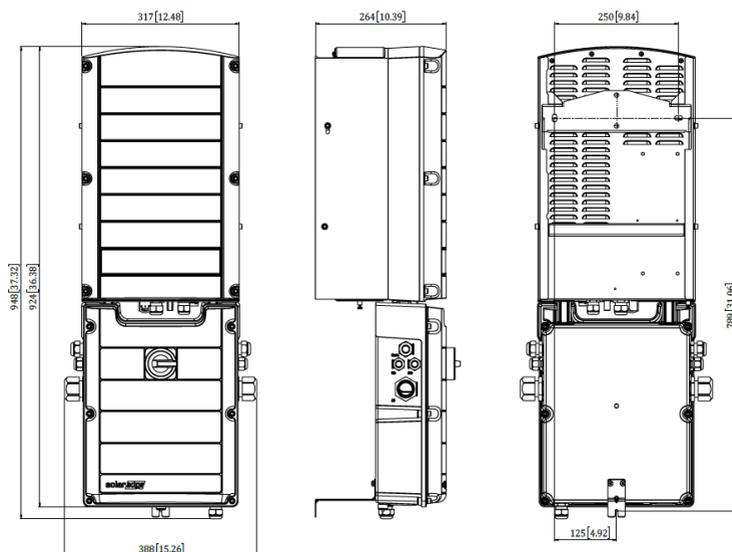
Unité principale et unité de couplage - avant, côté et arrière
